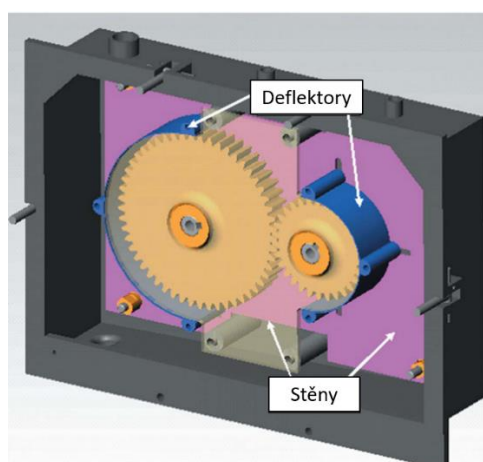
Příklad testovacího zařízení s otevřeným okruhem (upraveno) [3]
